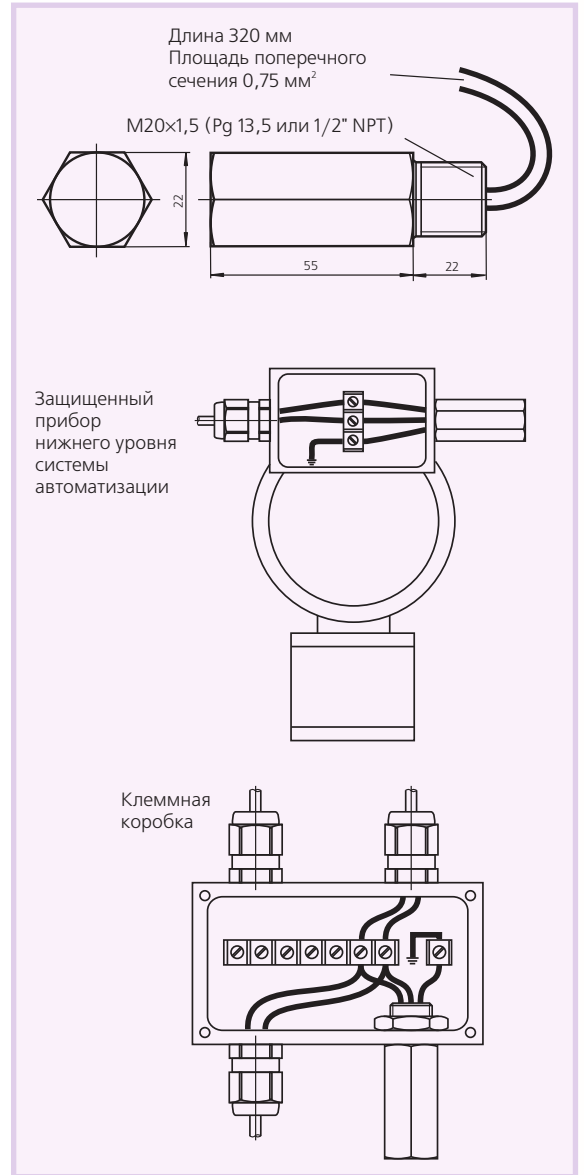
Габаритные размеры устройства F*-LB-I и примеры схем подключения его внешних цепей при установке устройства на корпусе защищаемого прибора и в клеммной коробке
